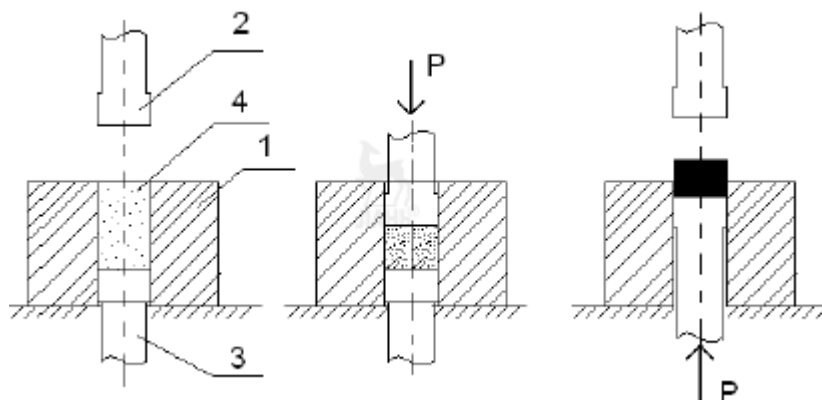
Схема одностороннего прессования: а – засыпка порошка и установка пуансона; б – прессование порошка в изделие; в – выпрессовка изделия; 1 – матрица пресс-формы; 2 – верхний пуансон; 3 – нижний пуансон; 4 – прессуемый порошок
